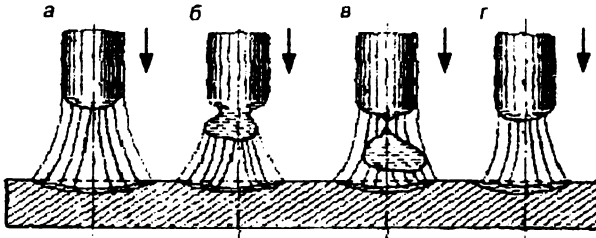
Схема переноса электродного металла через дугу при сварке длинной дугой:
